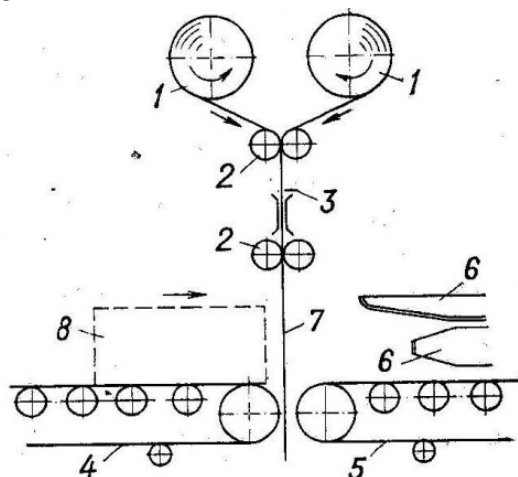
Принципиальная схема кипоупаковочного станка:
